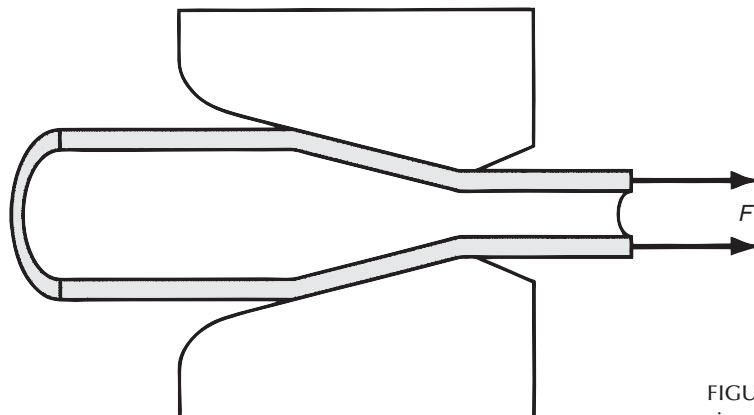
Estirado de tubos sin mandril (entallado de tubos).
